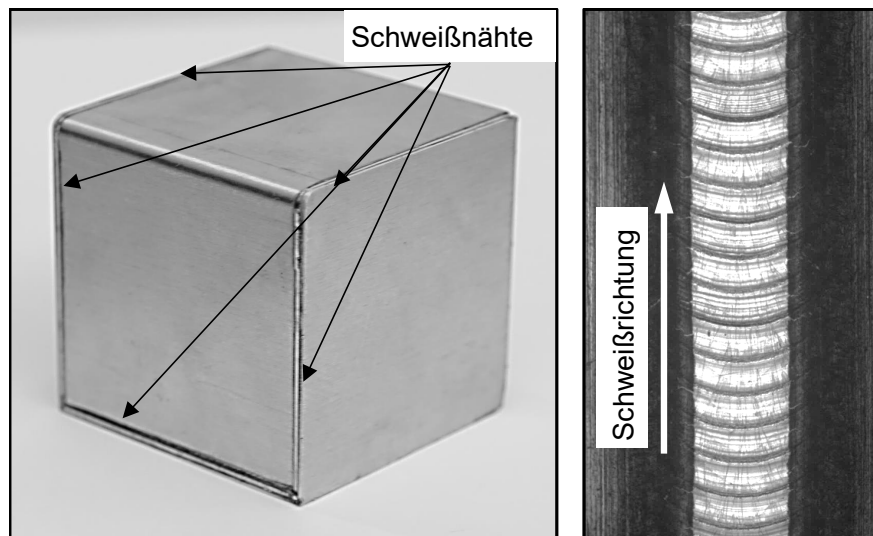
Geschweißtes Demonstratorbauteil und Nahtdraufsicht
